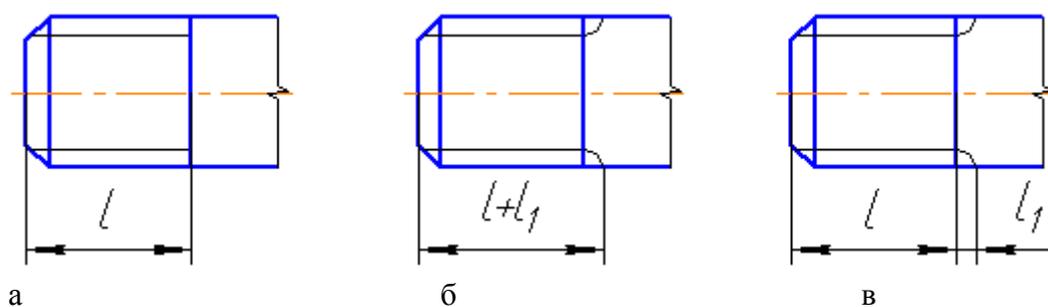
Изображение сбega резьбы, размер длины резьбы
